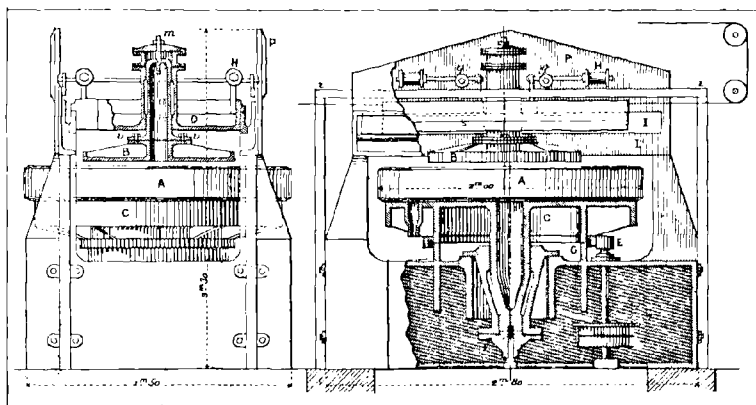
Machine à travailler mécaniquement les surfaces optiques.
